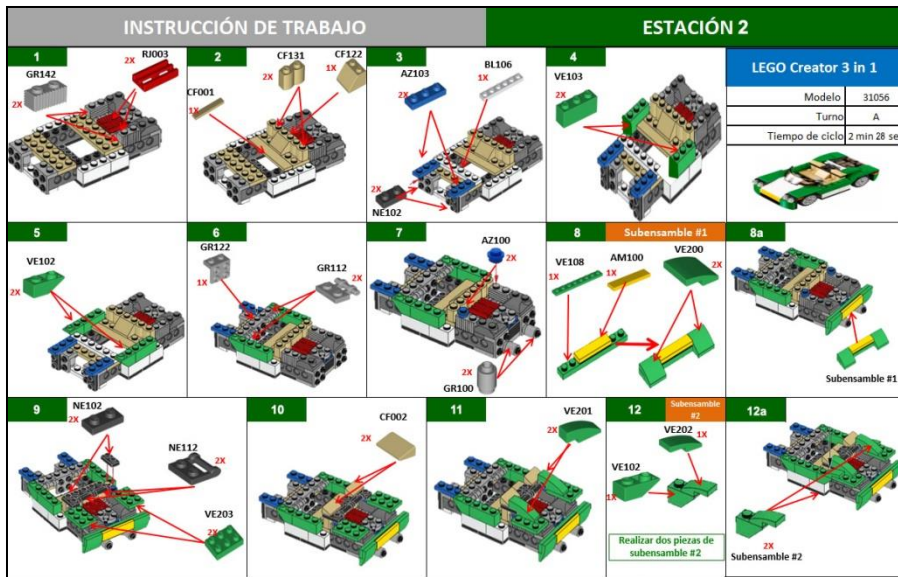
Ayuda Visual del Ensamble del Carrito LEGO
